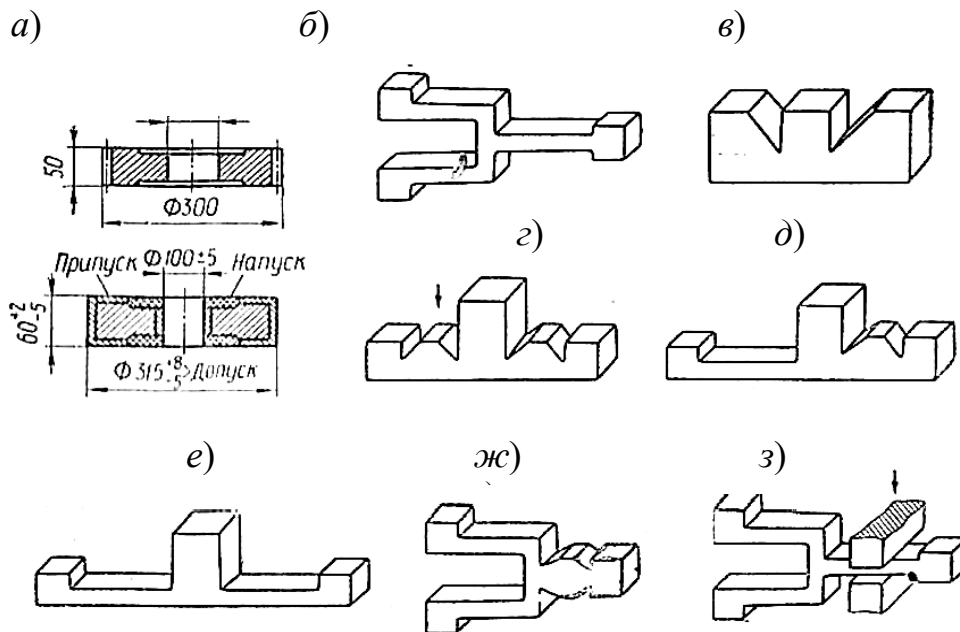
Чертеж поковки (а) и схемы процессаковки рычага с вилкой (б–з)
